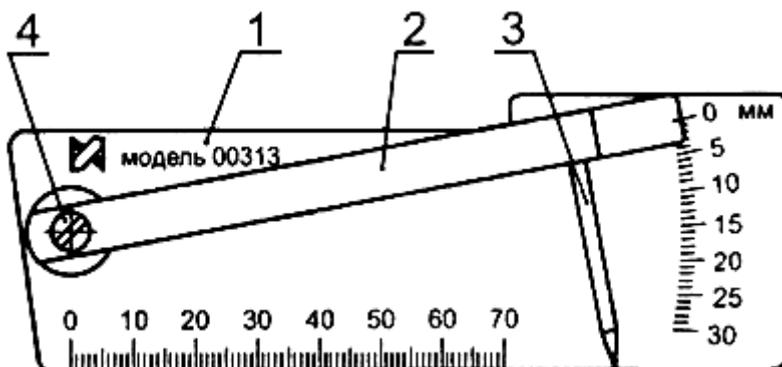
Общий вид приспособления для контроля глубины и диаметра поверхностных дефектов (1 - основание; 2 - планка; 3 - измерительный стержень; 4 - ось)
